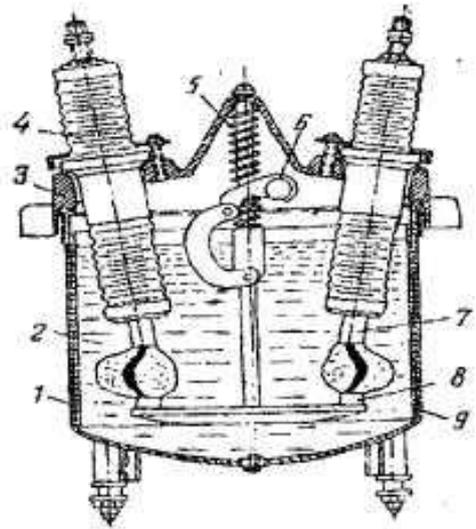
Схематический разрез масляного бакового выключателя ВМ-35: 1 - стальной бак, 2 - масло, 3- крышка, 4 - проходной изолятор, 5 - отключающая пружина, 6 - вал выключателя, 7 - неподвижные контакты, 8 - подвижные контакты 9 - изоляция стенок бака
